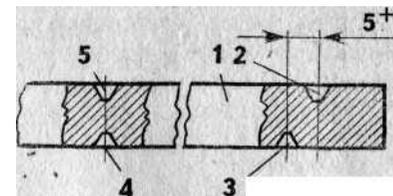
, 1 — торсион; 2 — старая лунка; 3 — новая лунка крепления рычага; 4 — старая лунка крепления торсиона; 5 — новая лунка.
